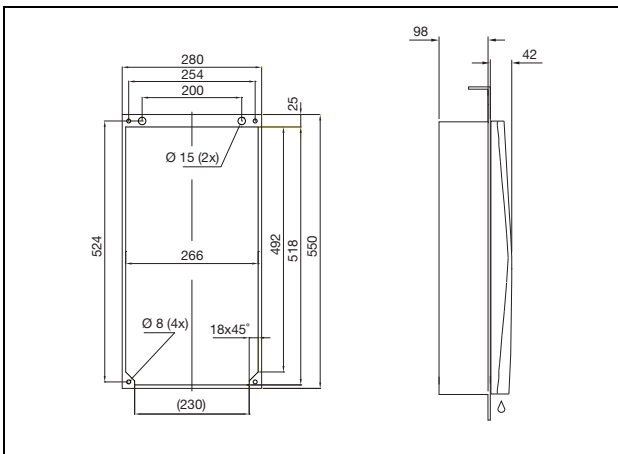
3328.xxx, 3329.xxx částečně zapuštěná montáž
